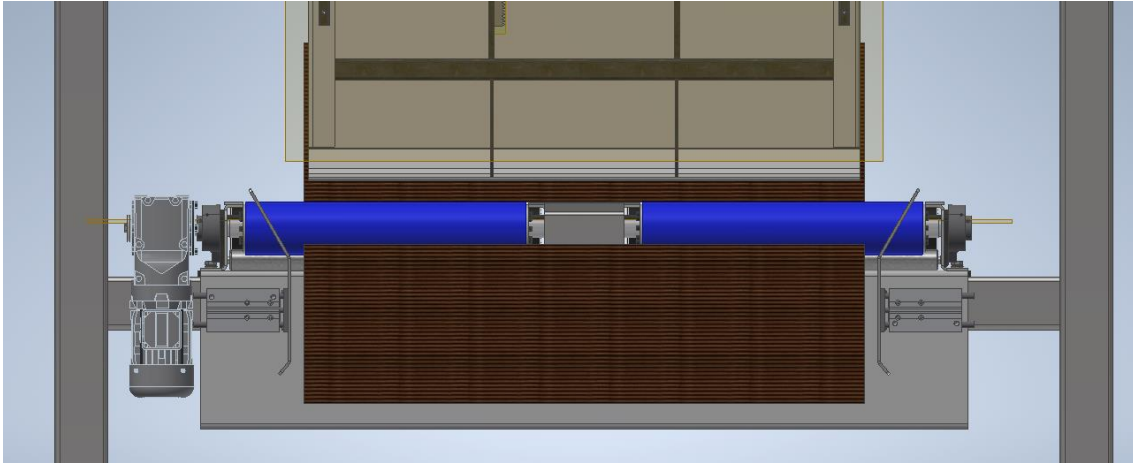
Vista frontal del centrador con la pila de cartón. Fuente: propia
